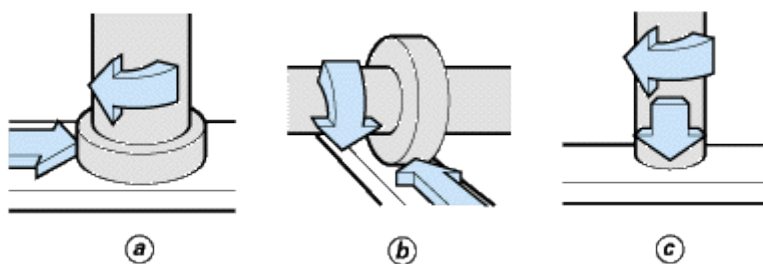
Surfacage, fraisage d'épaulements et fraisage axial
